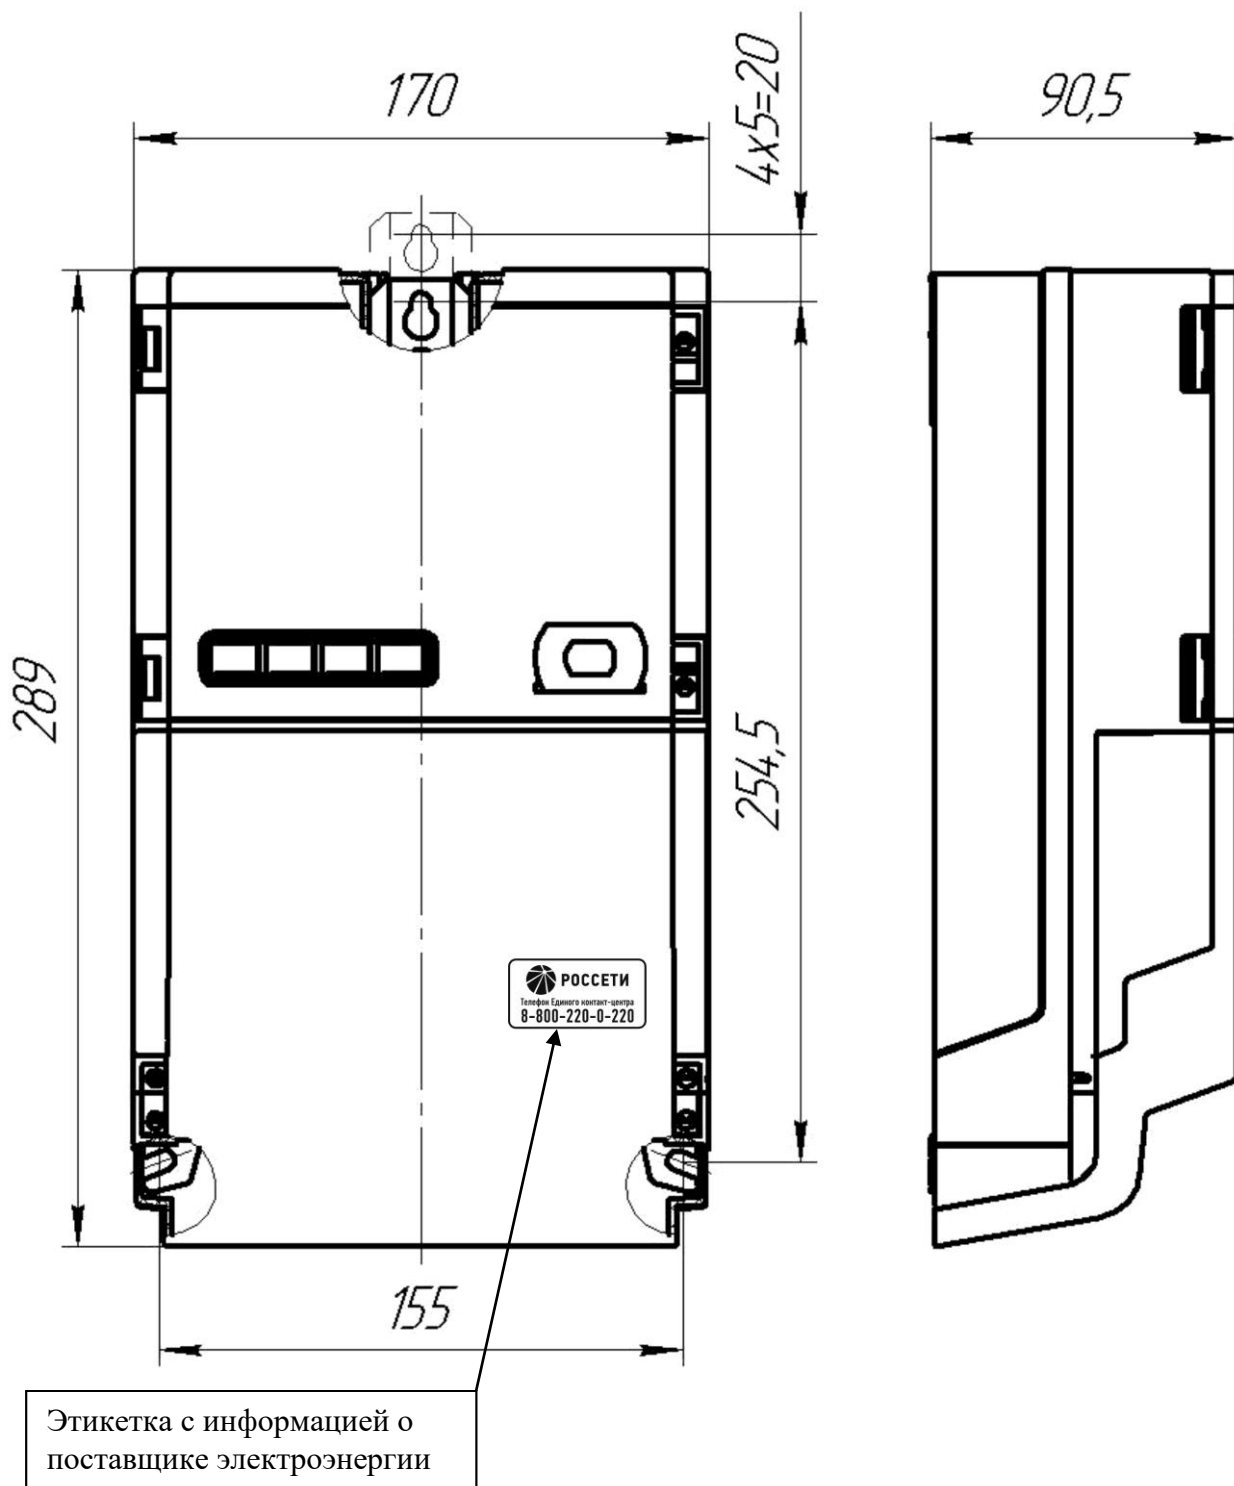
Габаритный чертеж и установочные размеры счётчиков, предназначенных для установки внутри помещения (таблица 1)
